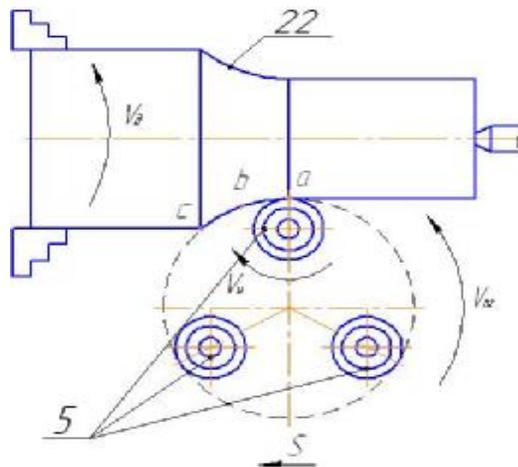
Схема работы приспособления для точения валов с планетарной головкой
